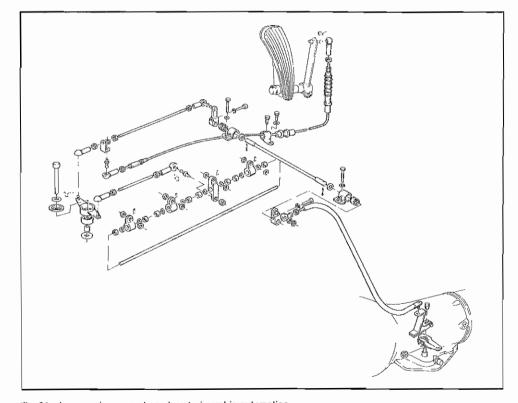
Leveraggio comando carburatori cambio automatico Control lever assy for automatic transmission carburettors
